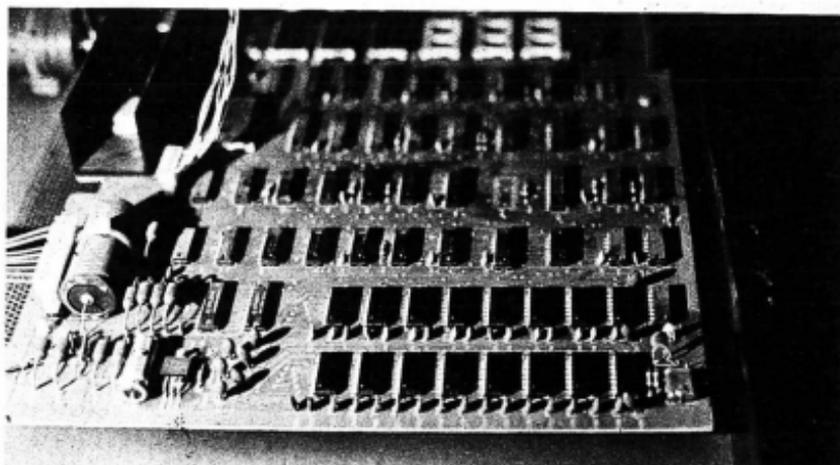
Placa de circuito impresso com integrados soldados.
